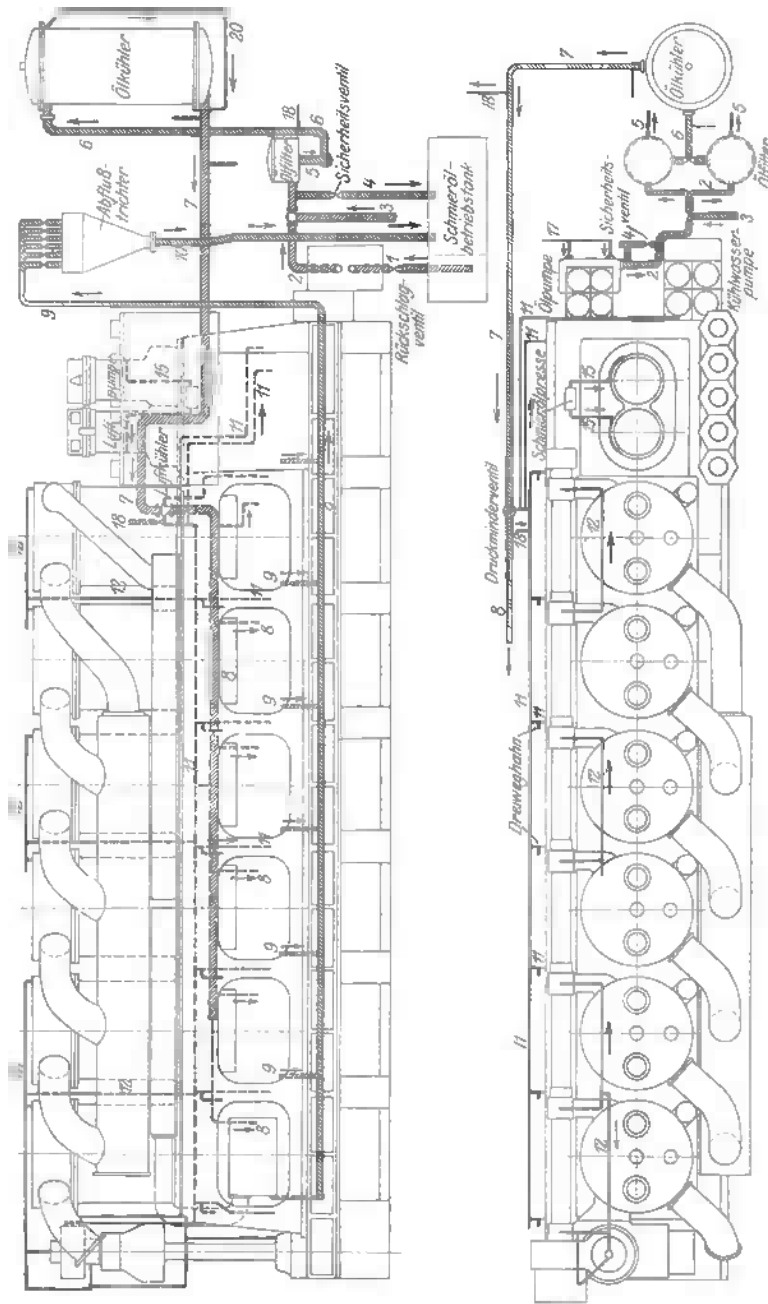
78. Schema der Schmieröl- und Ölkühlleitungen einer Tauchkolbenmaschine.
